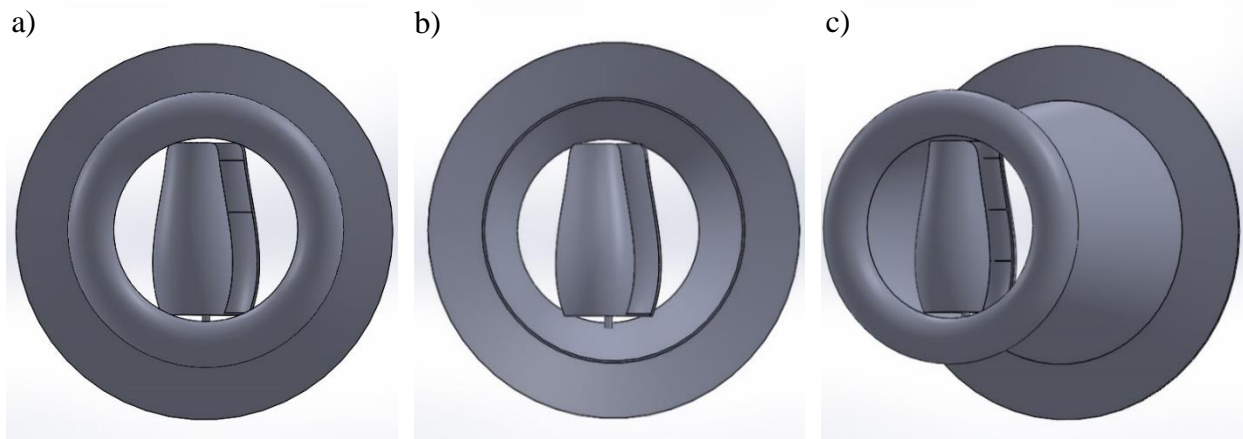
Ensamblaje de la turbina eólica de Tulipán con anillo difusor y $S=10\text{mm}$ (throat-brim): a) Vista frontal, b) vista posterior, c) Vista lateral. Diseñada con SolidWorks®.
